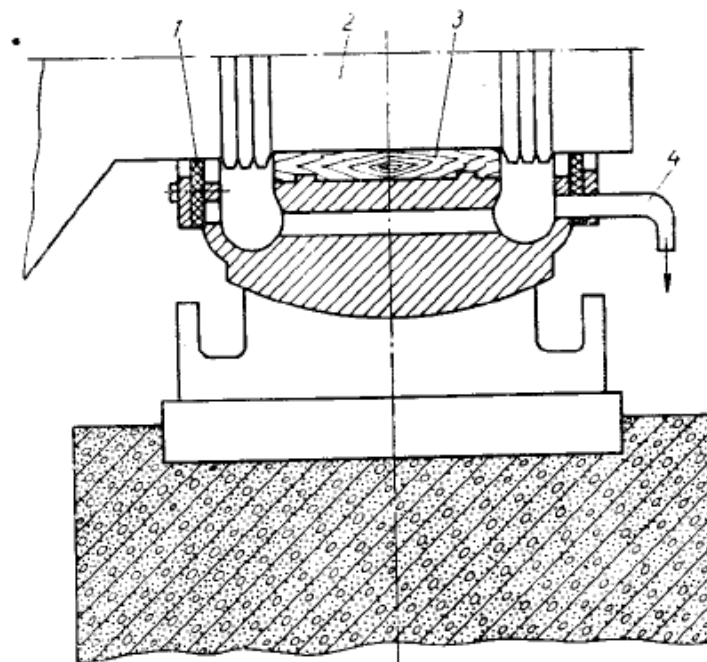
Схема розташування вкладиша у корпусі підшипника:
